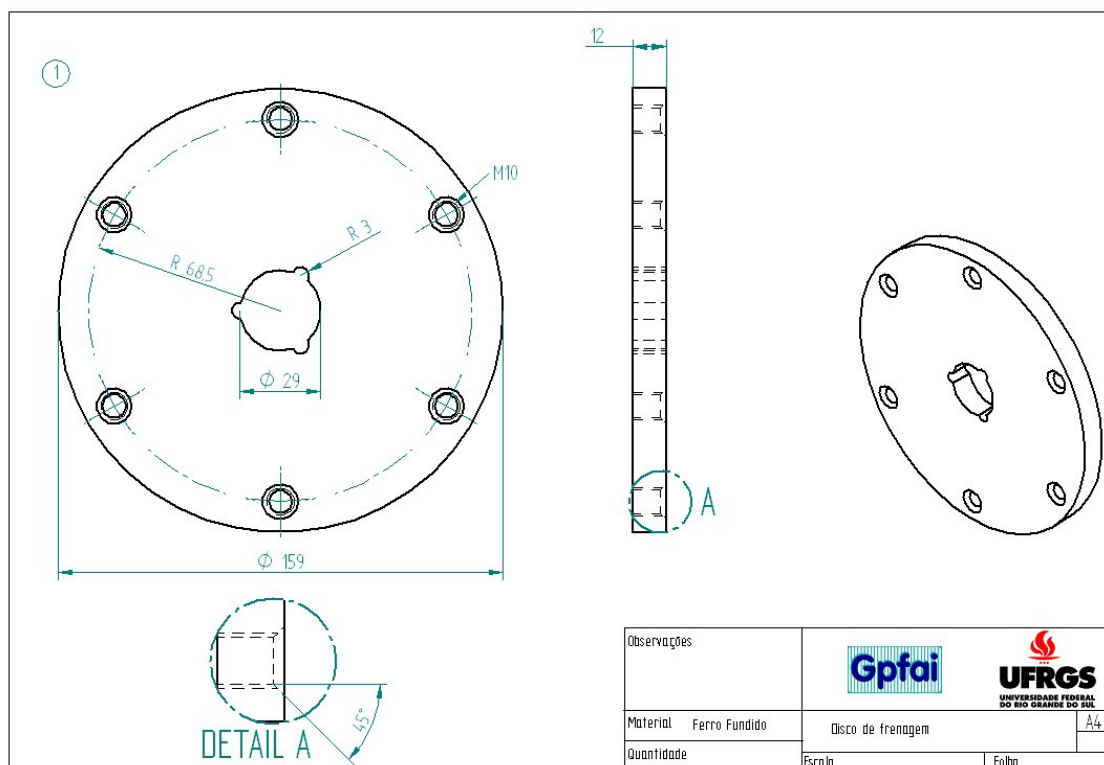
Desenho do disco dimensionado para o tribômetro.
